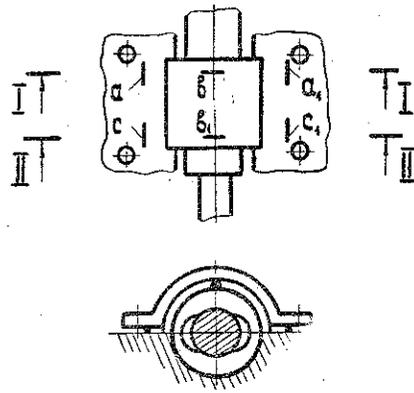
Расположение свинцовых проволок при проверке натяга вкладыша крышкой подшипника
